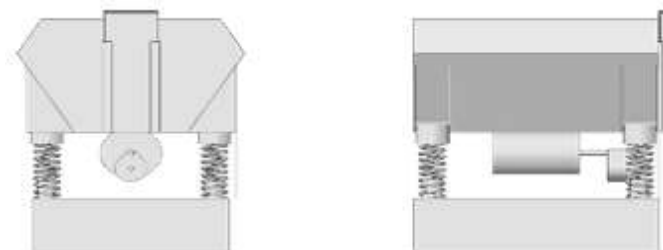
Vista frontal y lateral del primer diseño de la máquina.
